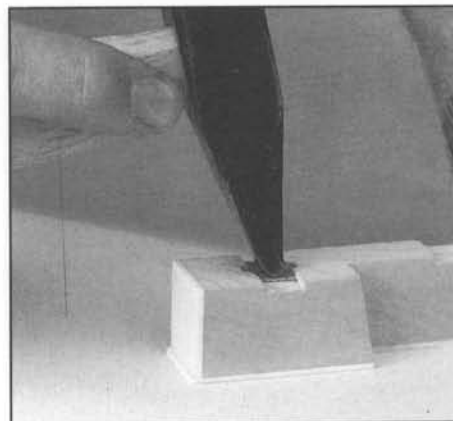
mit einem Hammer durch leichtes, vorsichtiges Klopfen geringfügig verringert.
